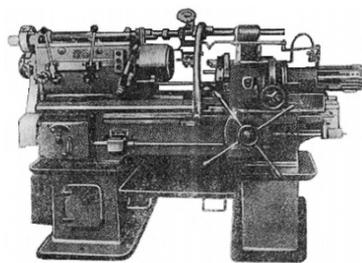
Токарно-револьверный станок модели 1336 выпуска 1934 г.
